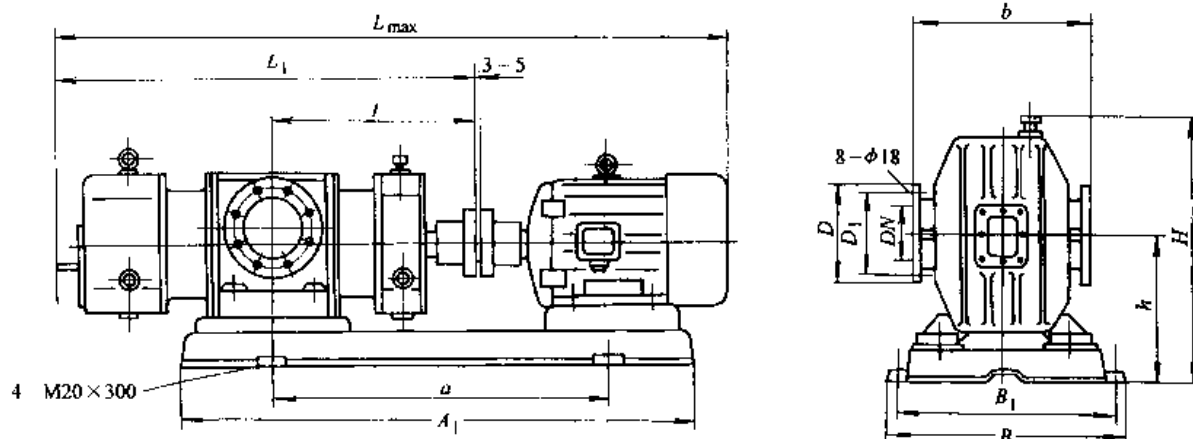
L41LD、L42LD、L43LD 罗茨鼓风机外形尺寸图
